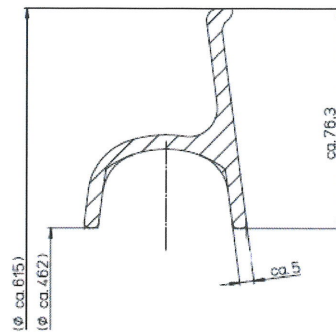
Vue en coupe joint rehausse – dalle de répartition
